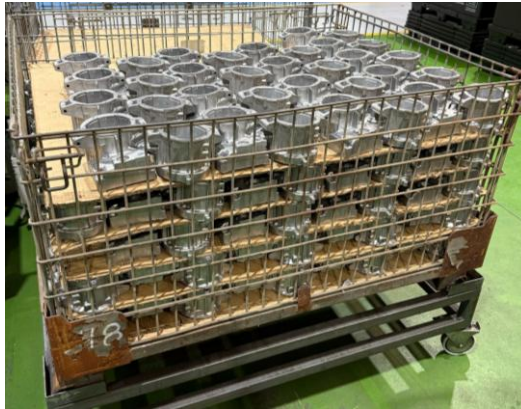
Contentor com peças *Motor Housing* 800V após fundição
